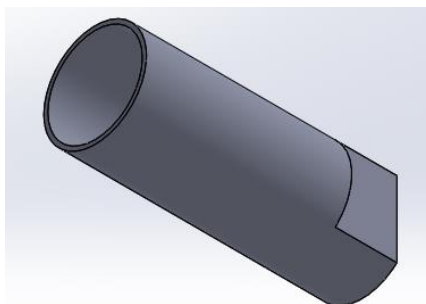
Desenho CAD do suporte do eixo rotativo para execução de atividade de corte
